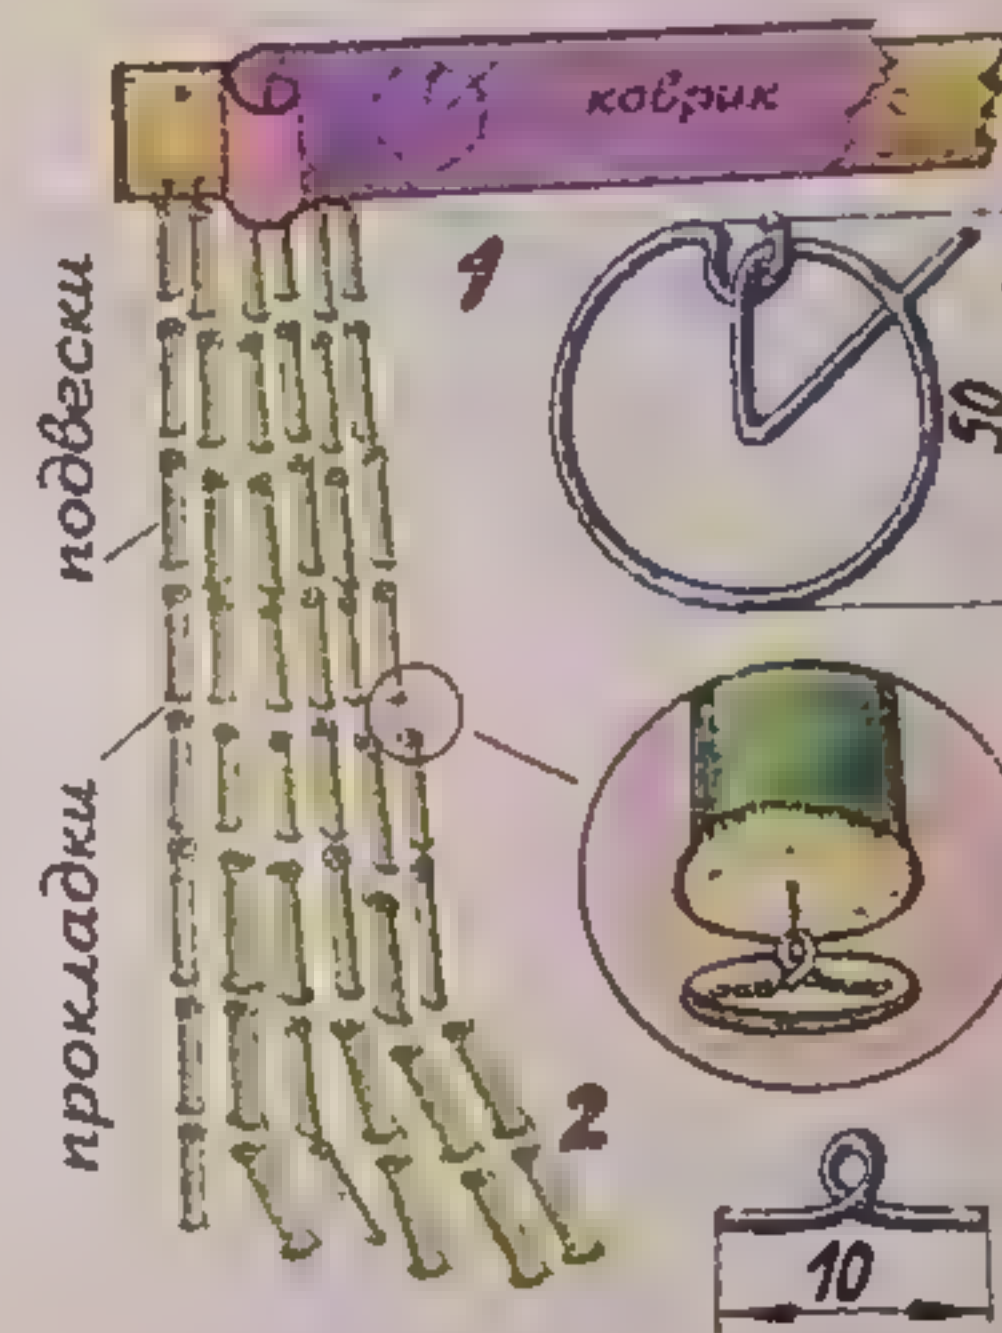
Штора в сборке: 1) пружина для крепления коврика, 2) стопорная петля из проволоки
